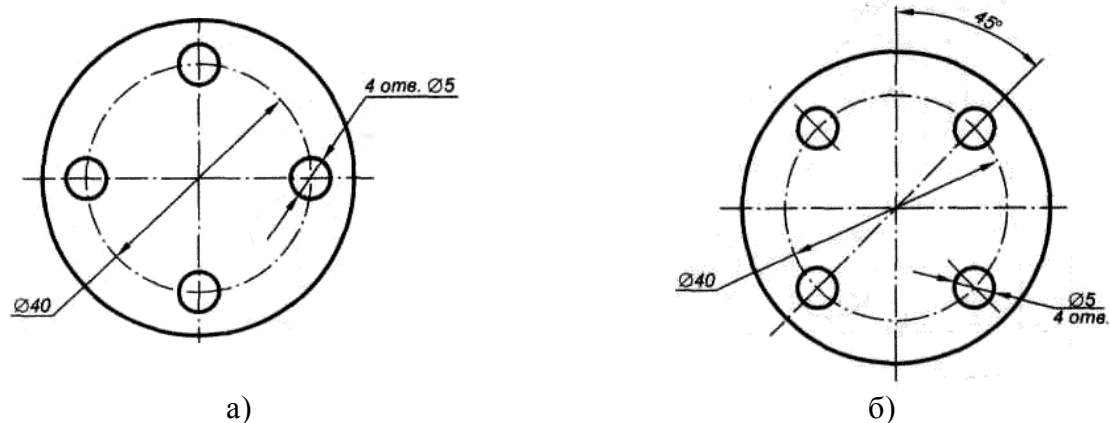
Нанесение размеров нескольких одинаковых отверстий
